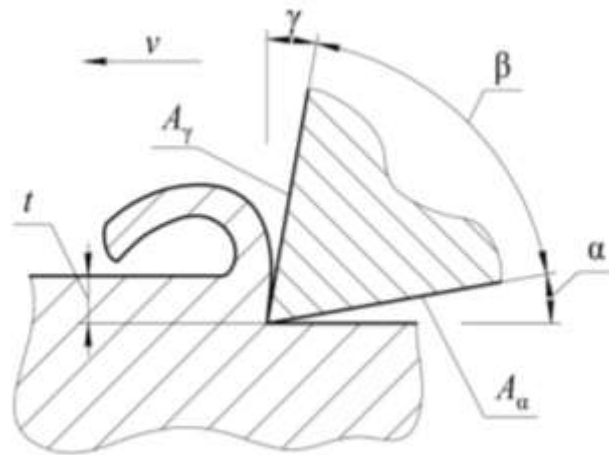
Ріжучий клин у процесі видалення стружки
